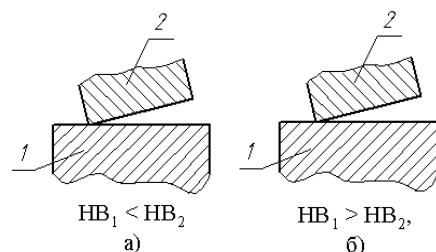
Прямая (а) и обратная (б) пара трения в зубчатой муфте:
